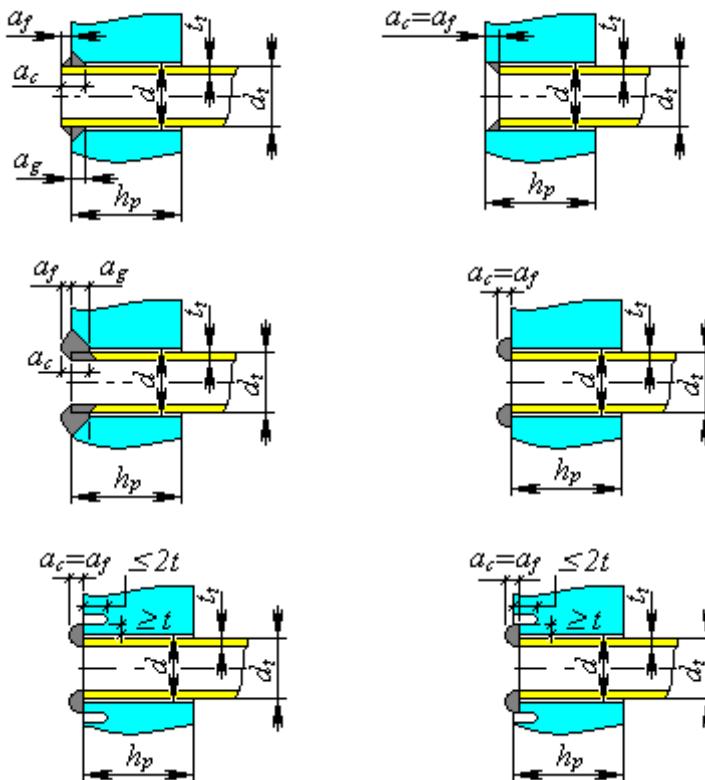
Крепление труб в решетке по ASME VIII-1
